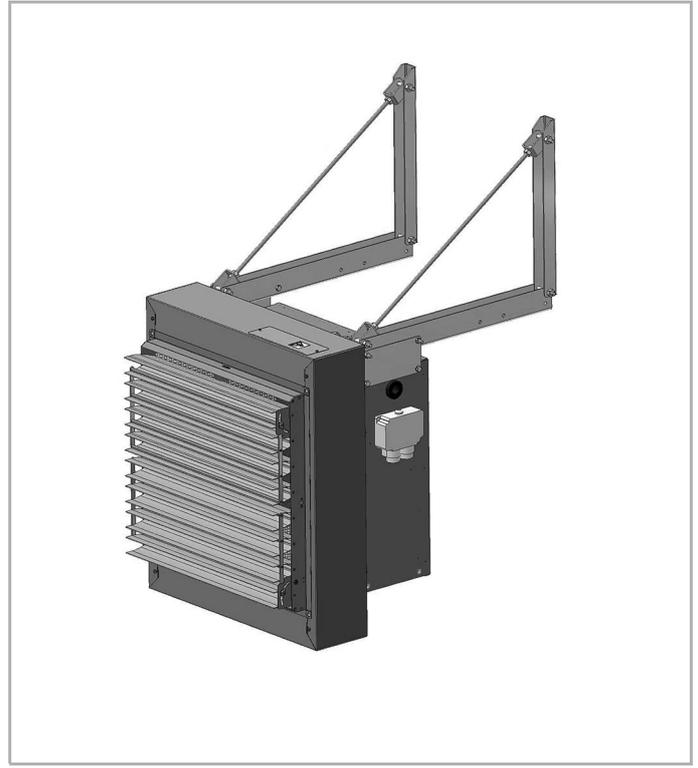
Montage mural de l'appareil en recyclage avec support « modulaire » (ZH#.550#)
